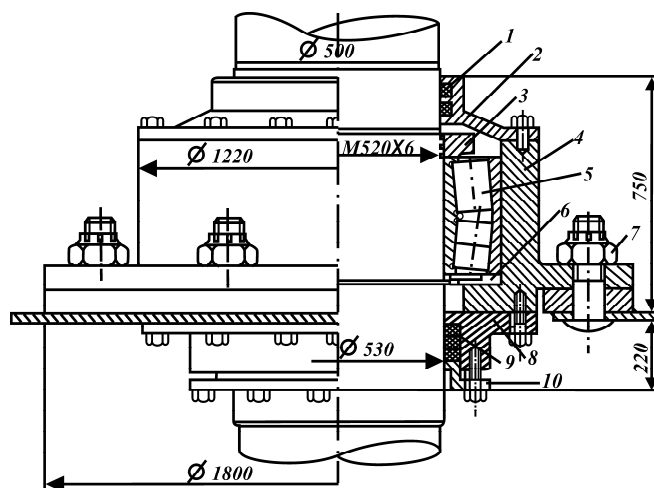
Опорный подшипник качения (роликовый) самоустанавливающегося типа
